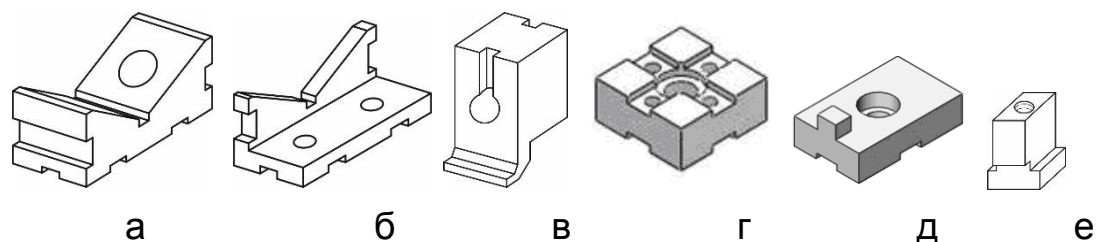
Примеры установочных деталей: а, б – призмы; в, г – опоры; д – установ для фрезы; е – шпонка Т-образная
